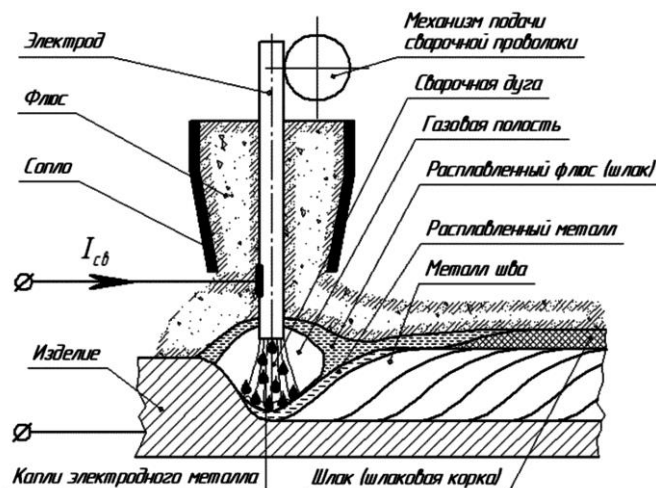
Схема автоматической сварки под флюсом
